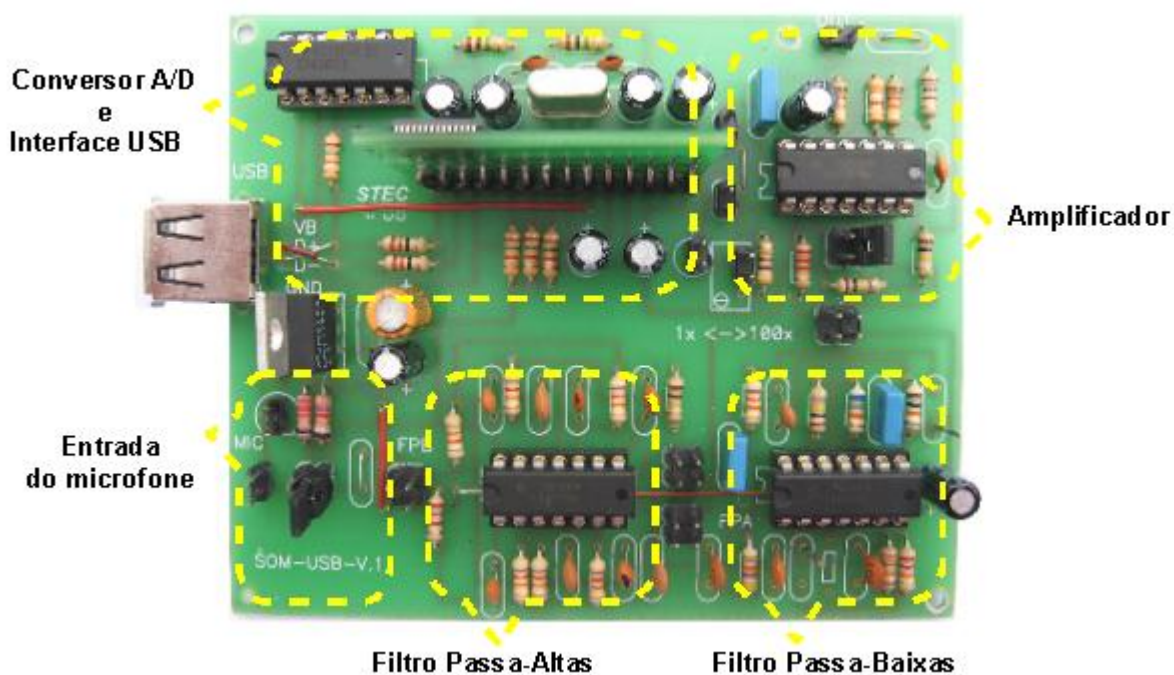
Placa de circuito impresso projetada para fazer a captação dos sons.
